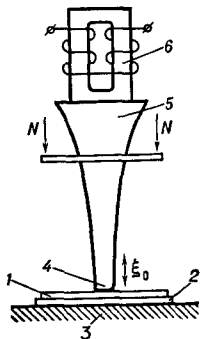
Схема установки для ультразвуковой сварки полимерных материалов: 1, 2 — соединяемые материалы; 3 — опора; 4 — сварочный наконечник; 5 — волновод-концентратор полуволновой или волновой длины; 6 — магнитострикционный преобразователь.
